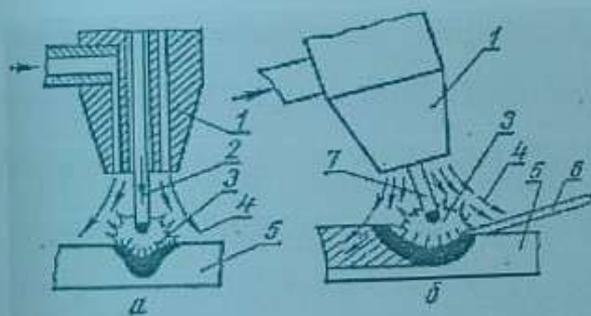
Схемы способов сварки (наплавки) в среде защитных газов:
